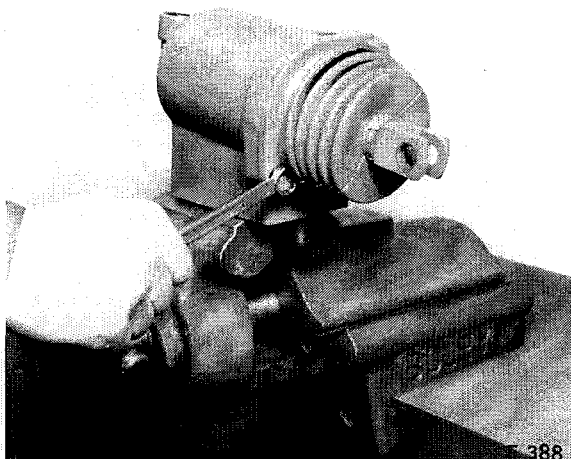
Lösen der Befestigungsschrauben für den Zylinderdeckel
